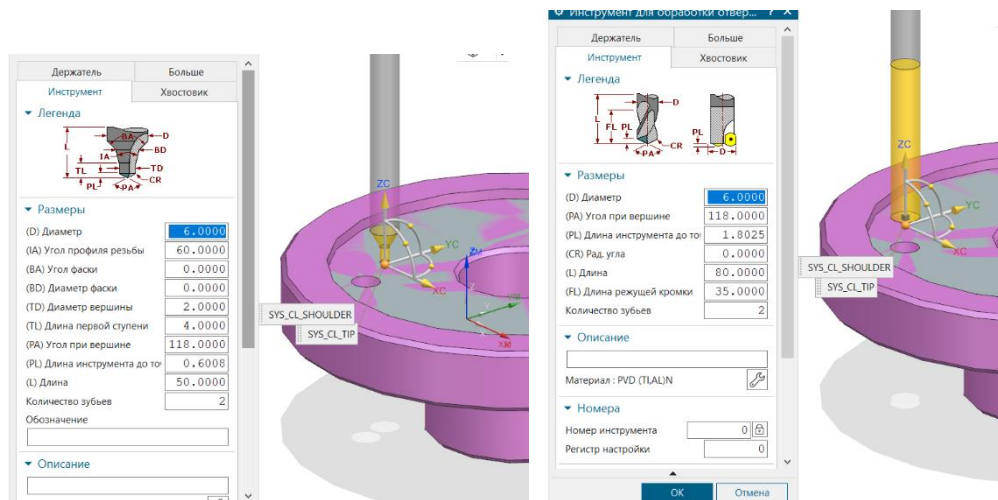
Вибір інструментів з визначеними параметрами
